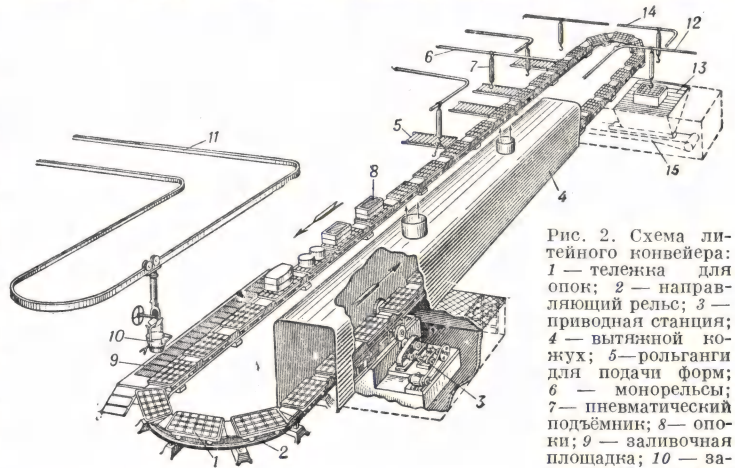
Схема литейного конвейера: 1 — тележка для опоки; 2 — направляющий рельс; 3 — приводная станция; 4 — вытяжной кожух; 5 — рольганги для подачи форм; 6 — монорельсы; 7 — пневматический подъёмник; 8 — опоки; 9 — заливочная площадка; 10 — заливочный ковш; 11 — монорельс для подачи ковша; 12 — монорельс для возврата опоки; 13 — выбивная решётка; 14 — монорельс для уборки литья; 15 — ленточный транспортер для возврата (с целью частичного нового использования) отработанной формовочной смеси.
